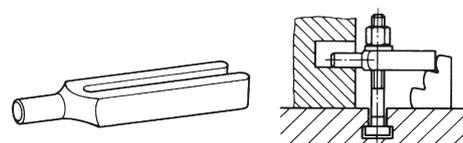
/76: Gabelspanneisen mit rundem Spannansatz
